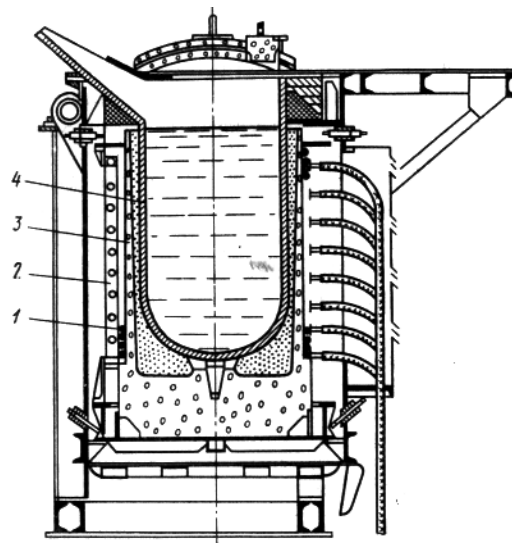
Схема и конструкция индукционной тигельной печи:
